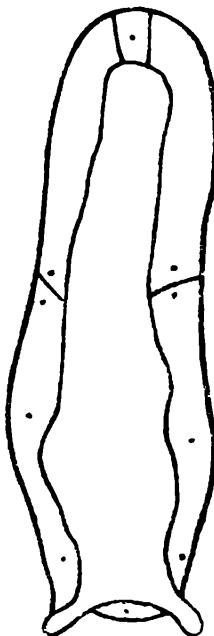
Схема расположения шпилек при обтяжке заготовки
